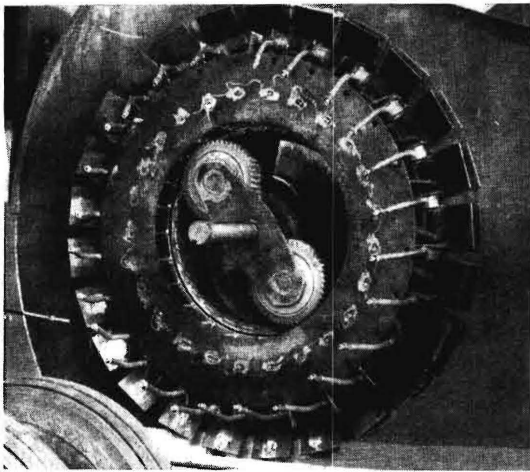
Gesamtansicht des Preßwerkzeuges der Brikettierpresse Lundell nach Entfernen der Stirnplatte mit dem Hauptlager. Am Umfang sind die Abweisbleche für die 25 austretenden Brikettstränge sichtbar.
